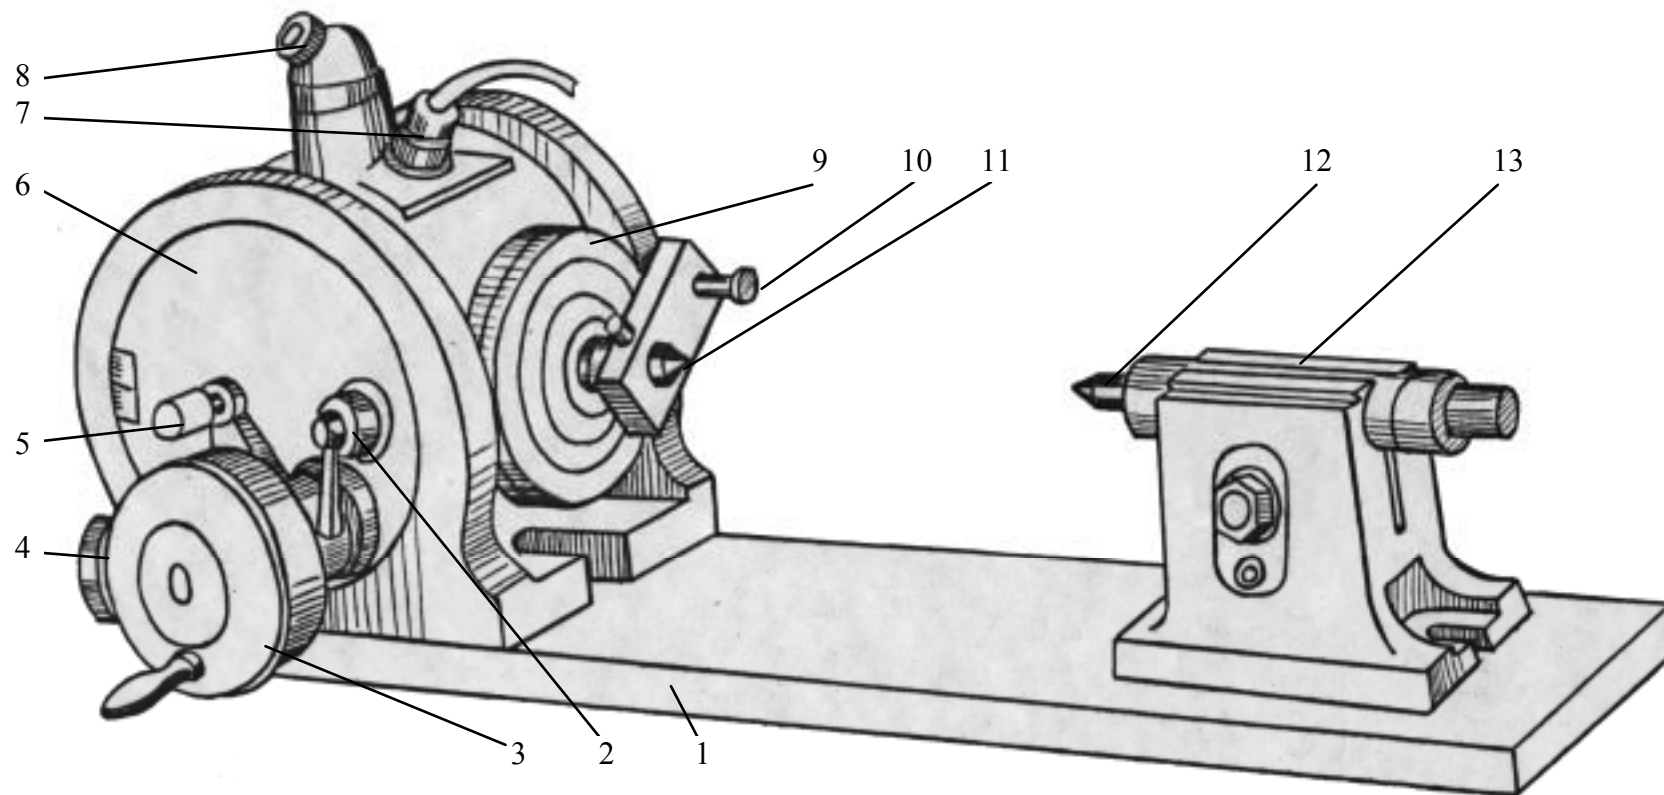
Общий вид делительной головки: 1 – станина; 2 – рукоятка зажима; 3 – маховик; 4 – микровинт; 5 – переключатель; 6 – корпус; 7 – осветитель; 8 – окуляр; 9 – наружная шкала; 10 – поводок; 11 – шпиндель; 12 – пиноль; 13 – задняя бабка
